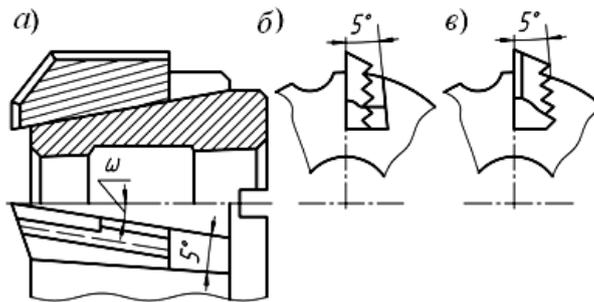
Крепление ножей сборных зенкеров рифлениями
